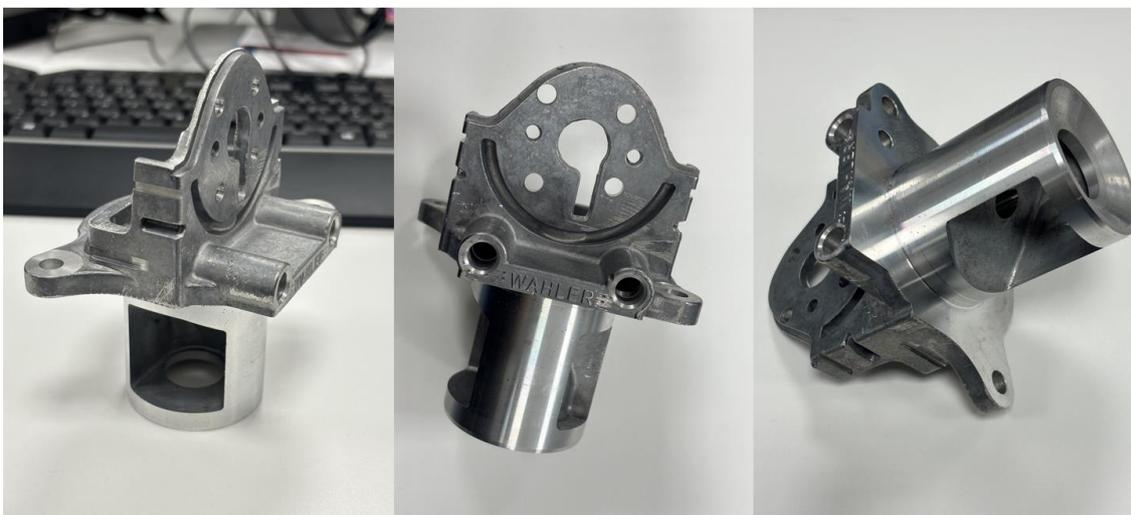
Exemplo de um housing (commodity de castings) que incorpora uma peça fabricada na BorgWarner para o cliente Daimler. Várias posições do mesmo housing.
